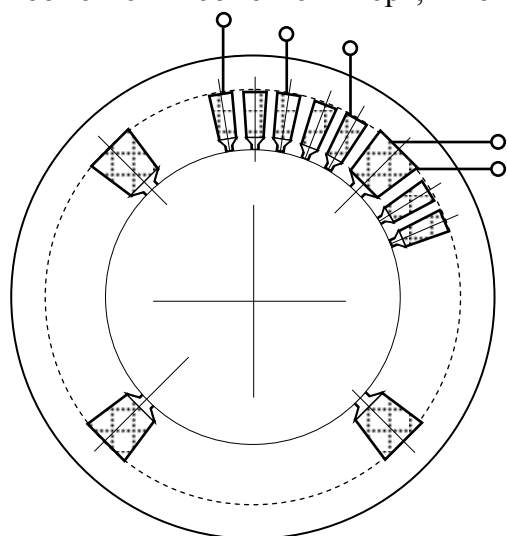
Схема конструкции статора разнотипно-полюсной индукторной машины
